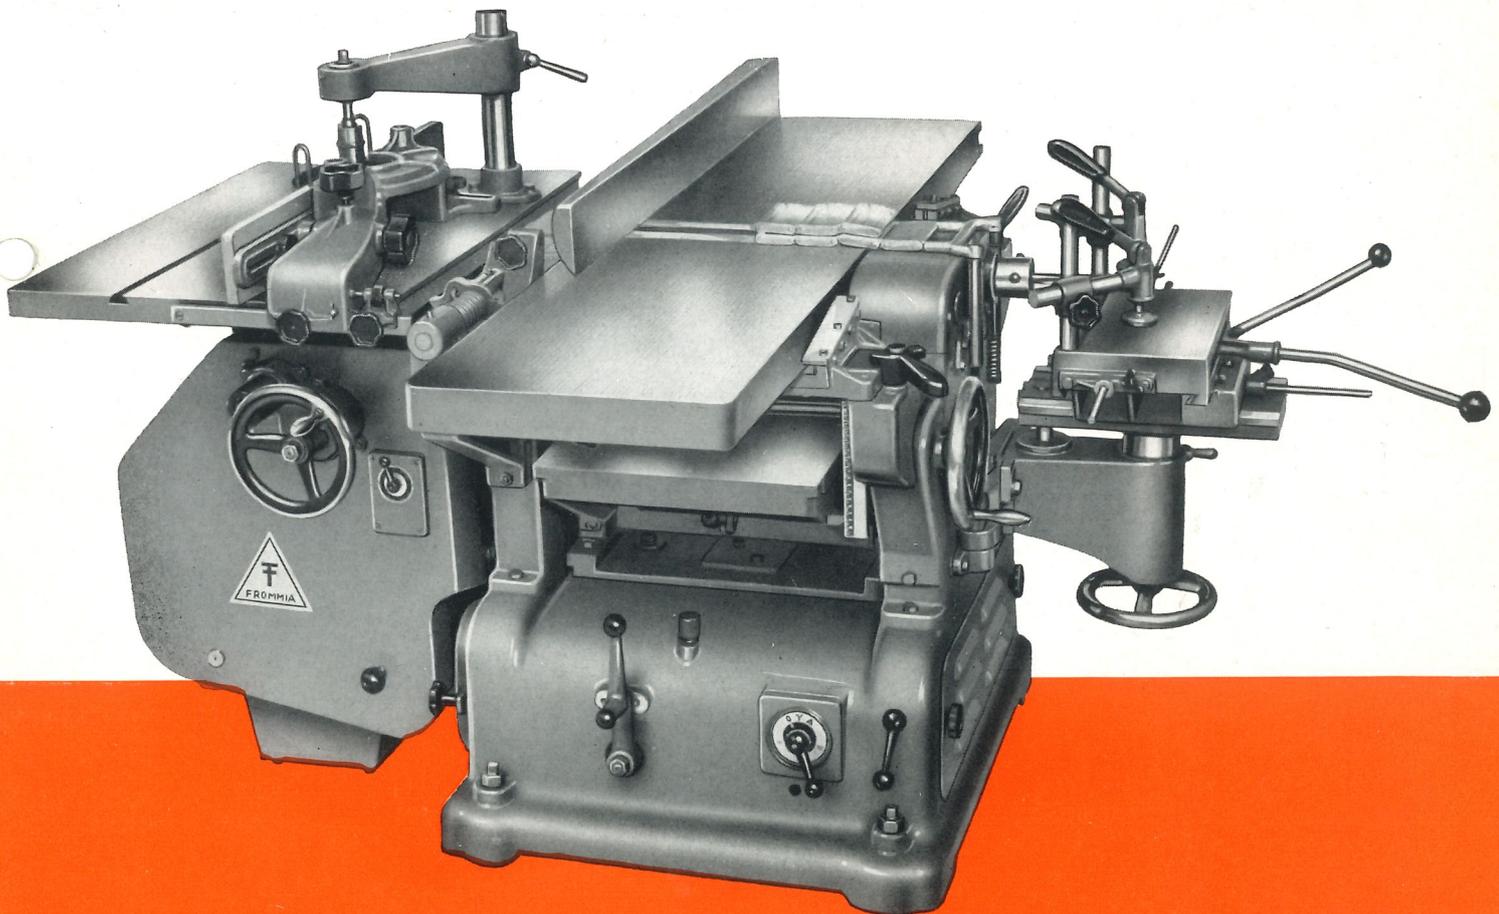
Nr. 261 UB. 5-fach kombinierte Abrichte, Dicke, Fräse, Kreissäge und Bohrmaschine mit 2 eingebauten Motoren
